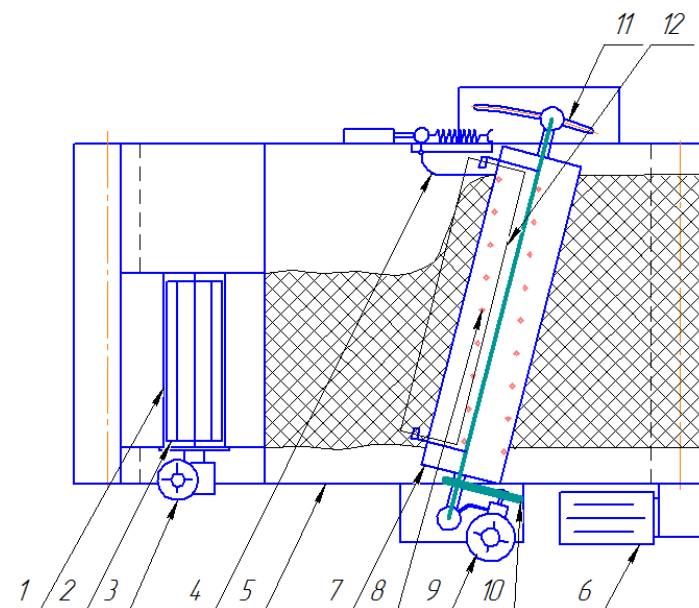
Разравнивающее устройство: 1 – бункер-дозатор, 2 – дозирующий вал, 3,6,9 – мотор-редуктор, 4 – концевая лопатка, 5 – лента конвейера, 7 – разравнивающий вал, 8 – пальцы, 10 – ременная передача, 11 – узел регулировки угла атаки, 12 – чистик.
